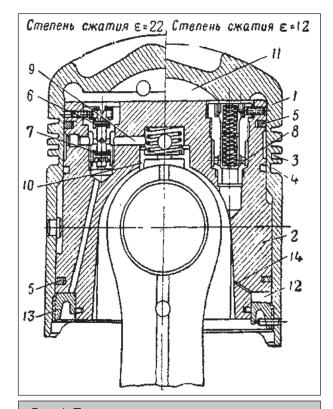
Поршень, автоматически регулирующий степень сжатия: 1 — подвижный стакан; 2 — внутренняя вставка; 3 — канавка под компрессионное кольцо; 4 — канавка под маслосъемное кольцо: 5 — уплотнительное кольцо; 6 и 7 — обратные клапаны: 8 — редукционный клапан; 9 — масляный канал; 10 — уплотнение; 11 - верхняя масляная камера; 12 — нижняя масляная камера; 13 — нижнее кольцо; 14 — дренажный канал
